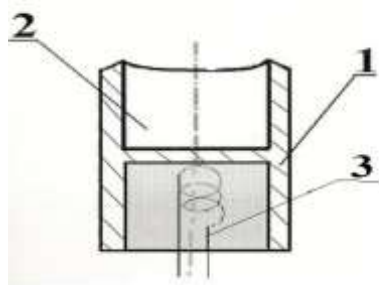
Конструкция МПК: 1-Корпус, 2-металлопористая губка, 3-нагревательный элемент [9]
